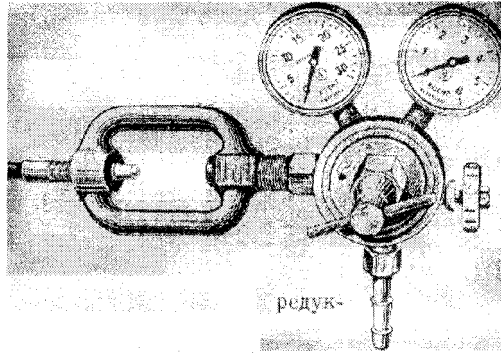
Ацетиленовый редуктор РД-2А
